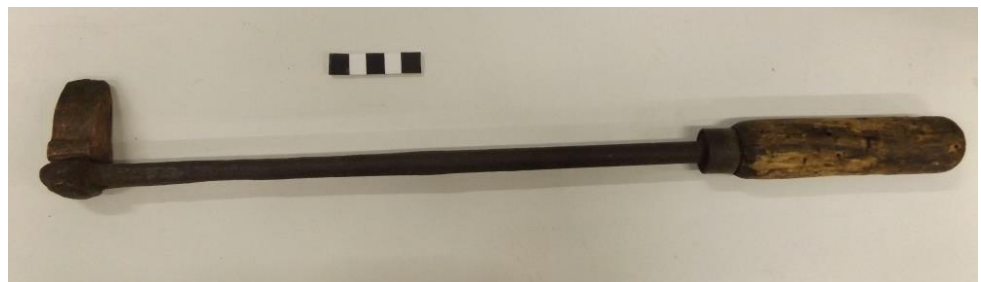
Ferro de soldar (Fonte: Imagem da autora)
